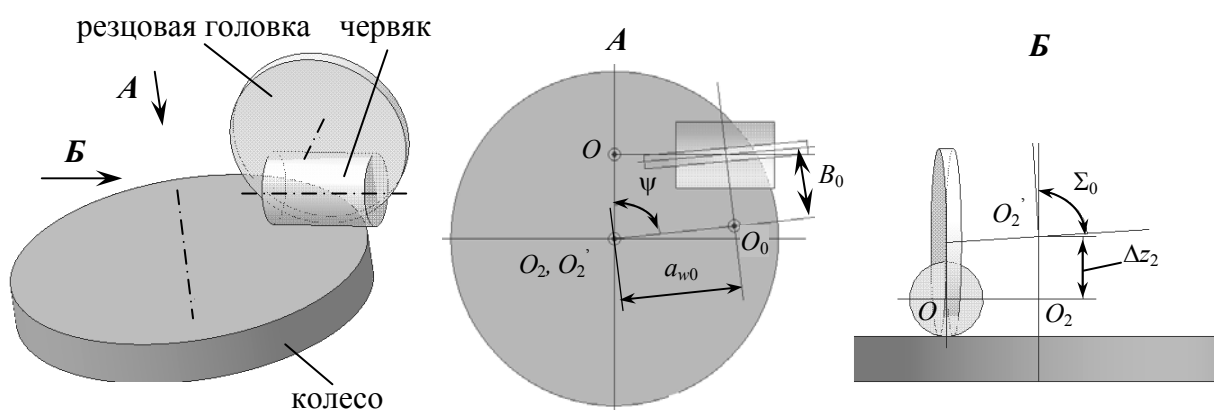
Воображаемое общее зацепление червяка, колеса и резцовой головки
